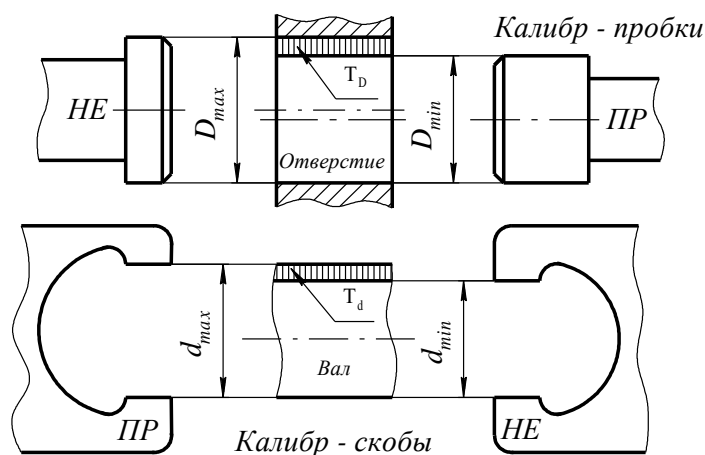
Схема контроля деталей гладкими предельными калибрами.
